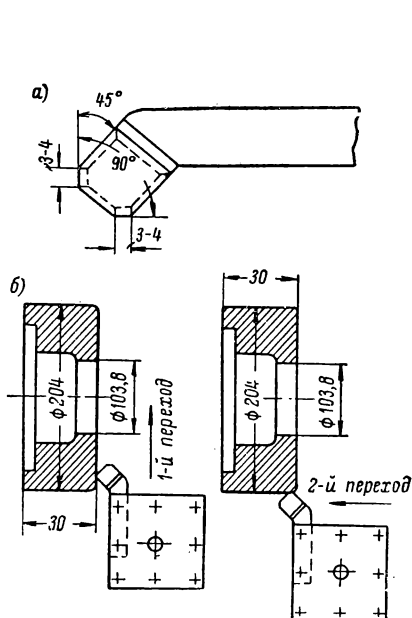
Применение комбинированного резца для чистового обтачивания наружной цилиндрической и торцевой поверхностей.
